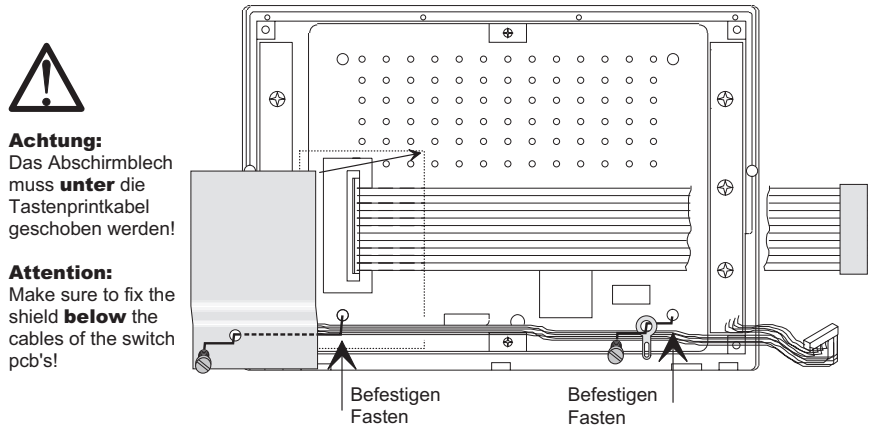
Befestigen des Abschirmblechs und der Lötflamme
